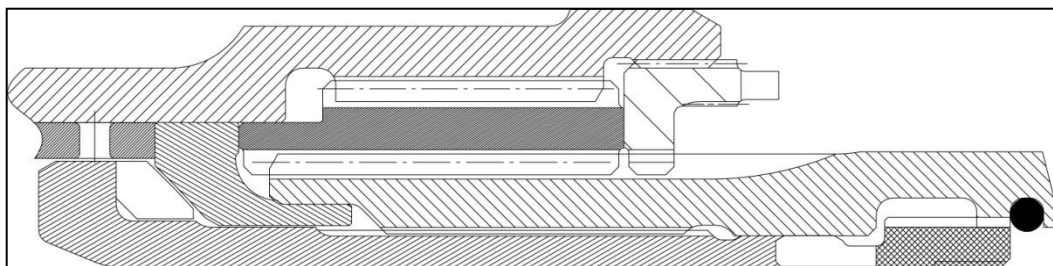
Шлицевая муфта в соединении роторов КВД и ТВД двигателя ПС-90
